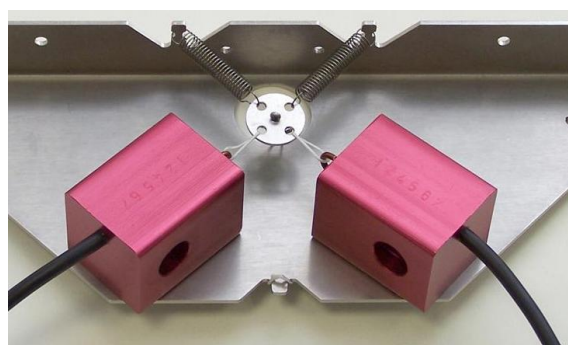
Fixação dos sensores de força no grupo de montagem de molas
